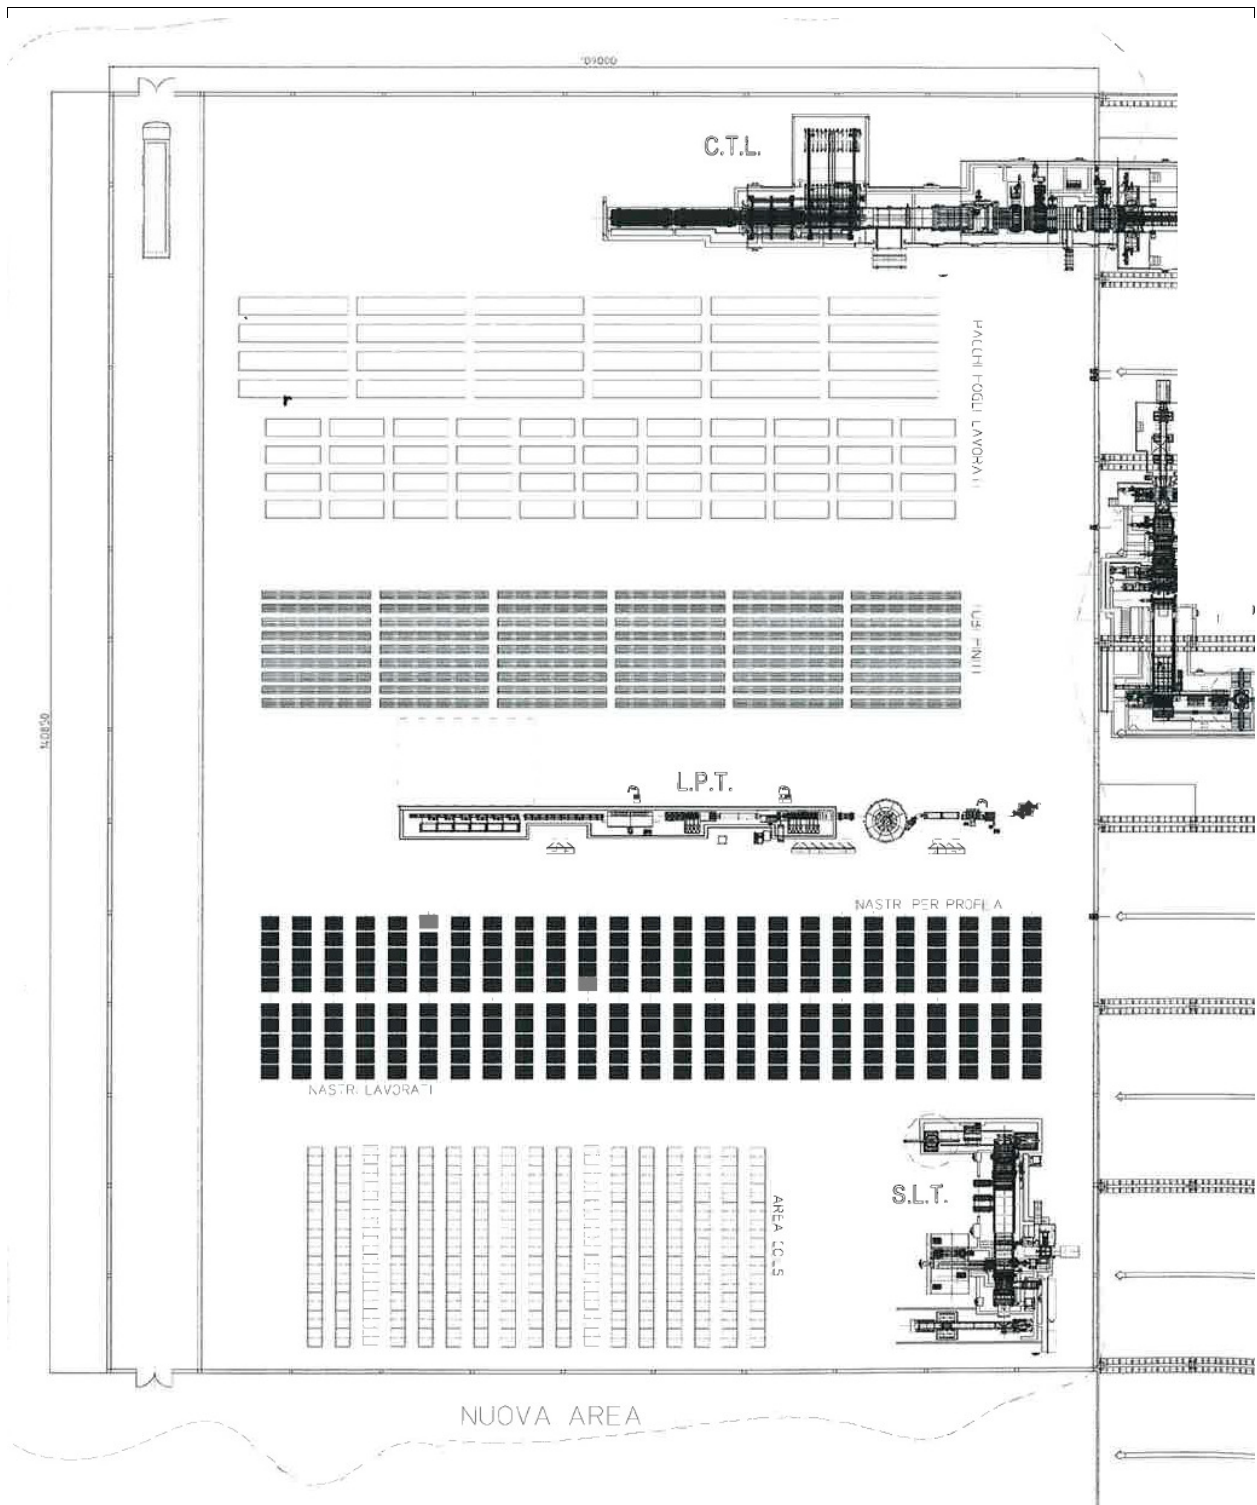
layout di progetto della nuova area con l'ubicazione degli impianti e dei materiali
